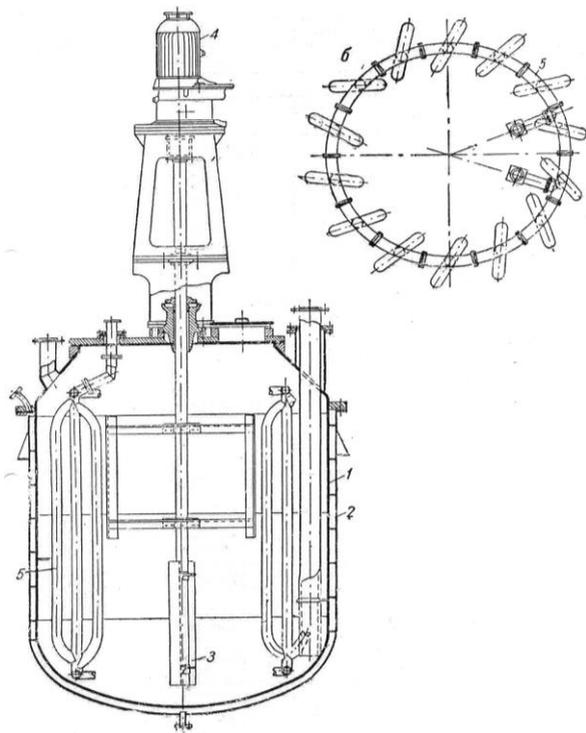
Конструкция реактора-полимеризатора для низкотемпературной полимеризации в эмульсии: 1- корпус; 2- рубашка; 3- перемешивающее устройство; 4- мотор-редуктор; 5- змеевиковый холодильник; 6- проходные и глухие фланцы
